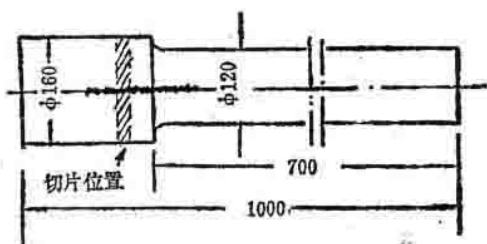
40Cr 轴粗加工尺寸及缺陷位置
